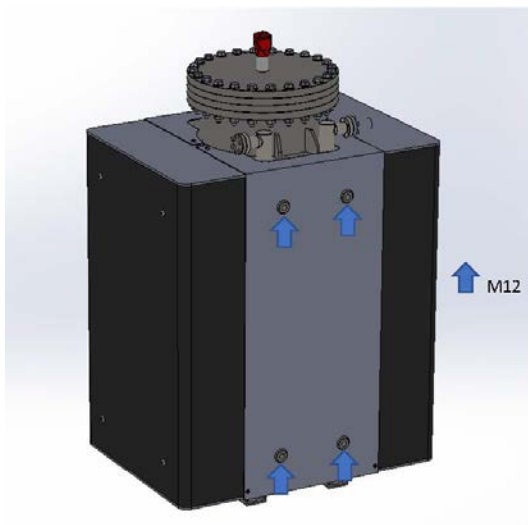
VIP 800 zeigt M12 Gewindebolzen
